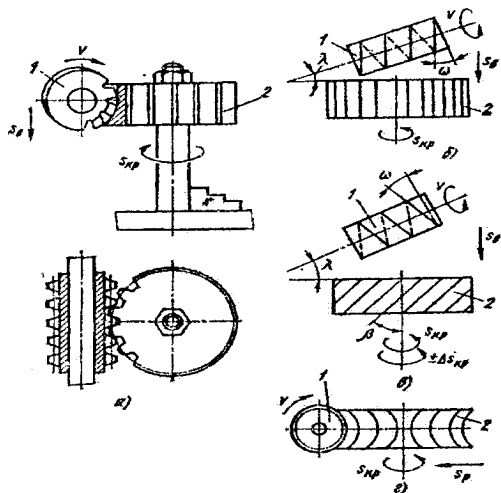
Фрезерування черв'ячною фрезою
